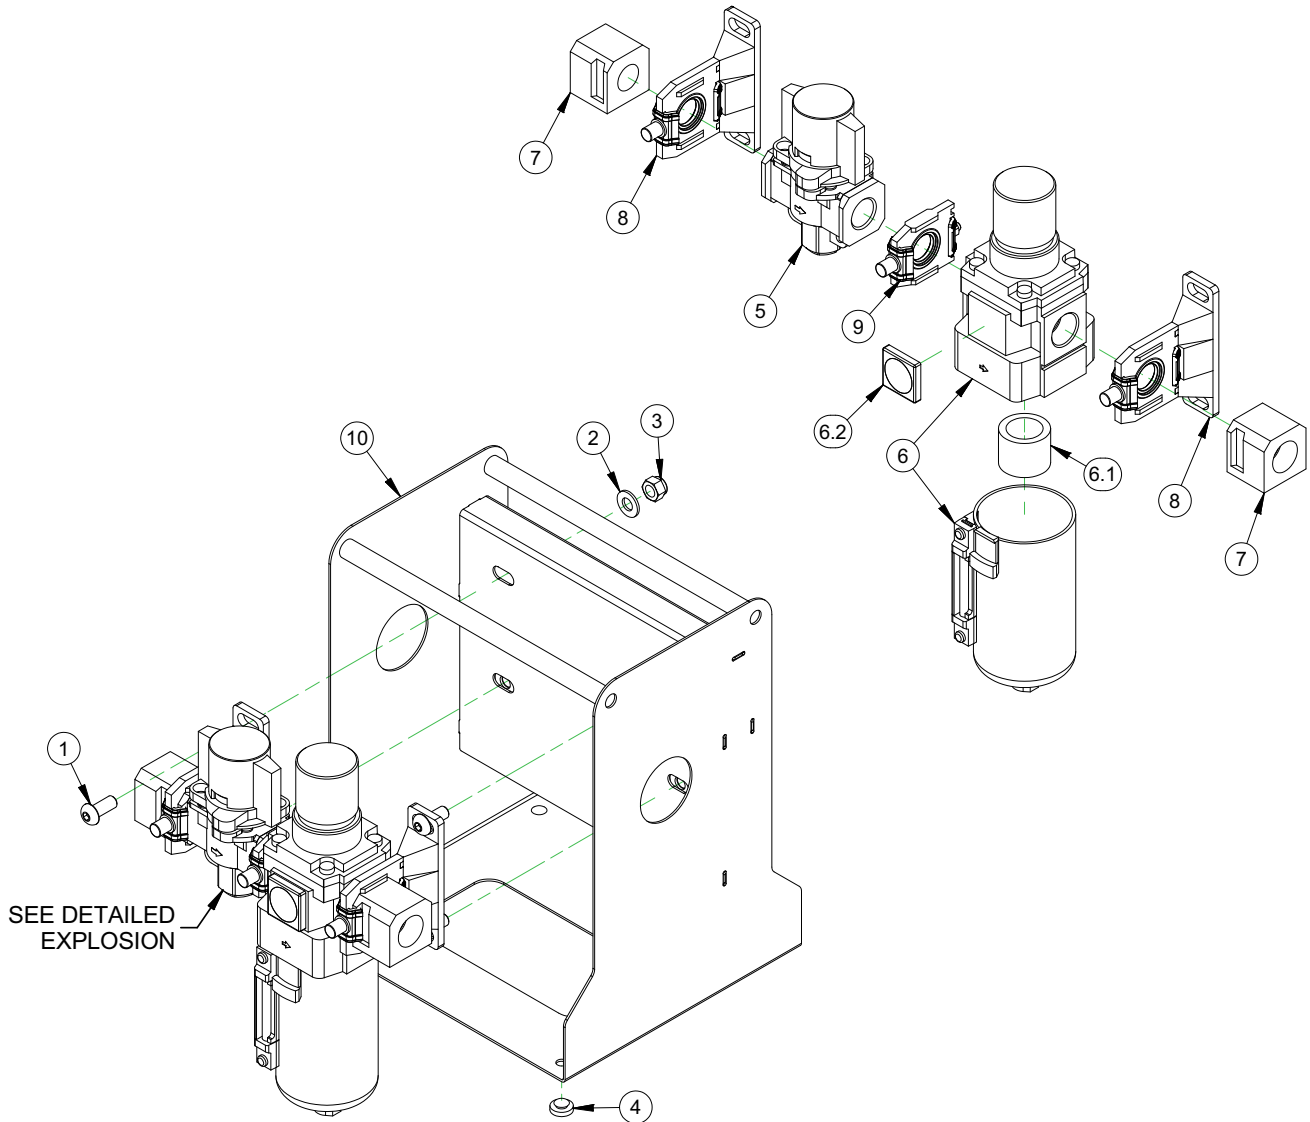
LISTE DES PIÈCES D'ASSEMBLAGE À POINT UNIQUE (P/N 62037)
